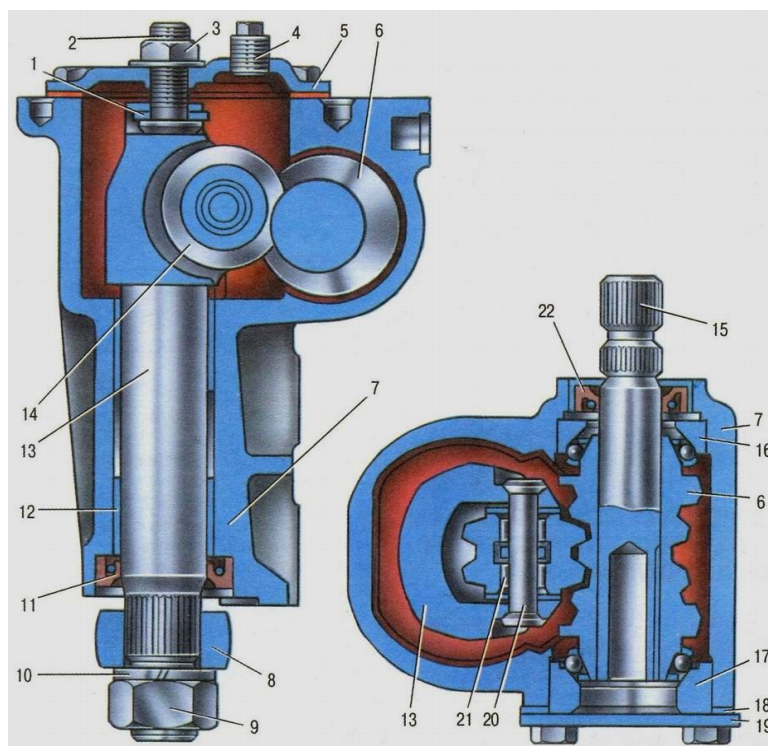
Схема картеру рульового механізму ВАЗ-2106:
